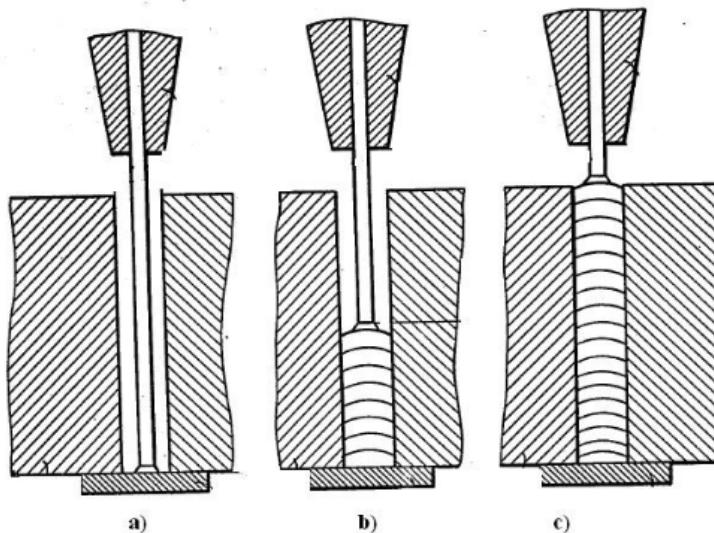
Soldagem em chanfro estreito com técnica do tipo II: a) passe de raiz; b) passe de enchimento; c) passe de acabamento [16]
